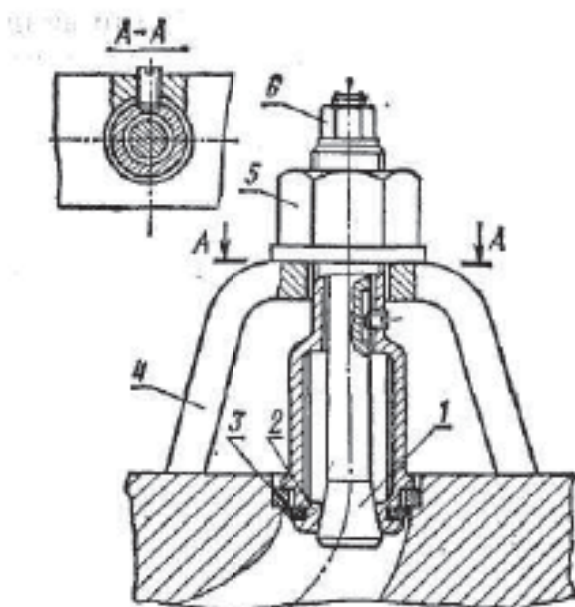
Знімач для випресовування сідла клапана з головки циліндрів.
